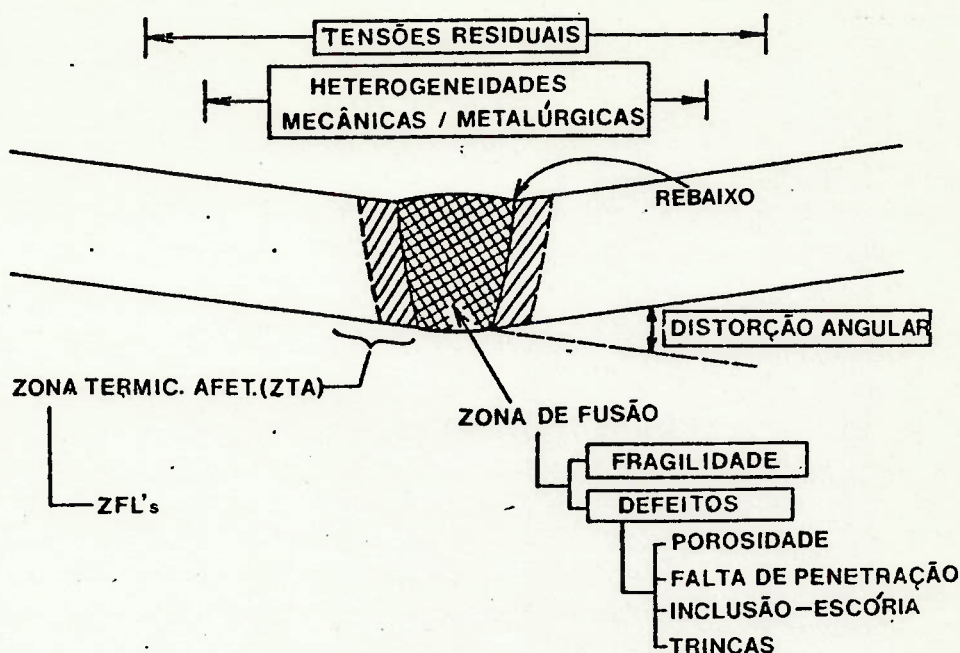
Características mecânicas de aços soldados (7).
